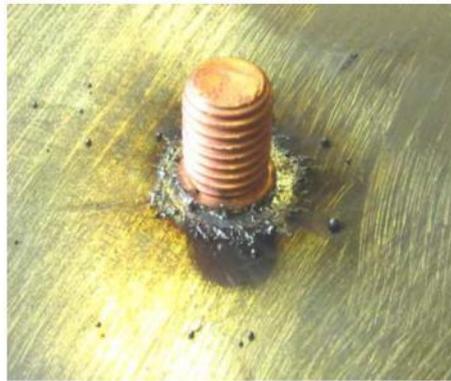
Schweißung mit zu hoher Energie, Spritzerkranz zu groß
